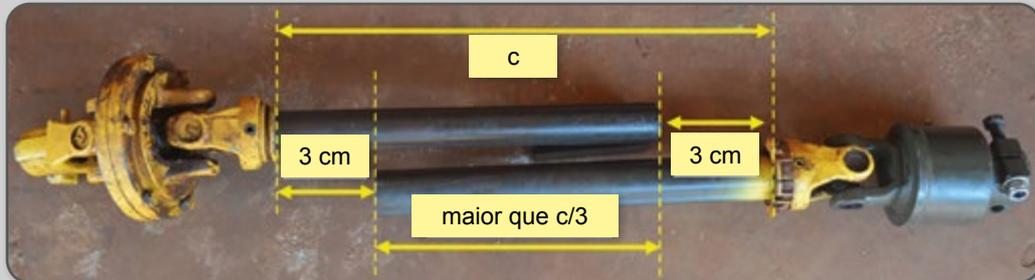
Partes do eixo cardã com folga de 3 cm em ambos os lados.
